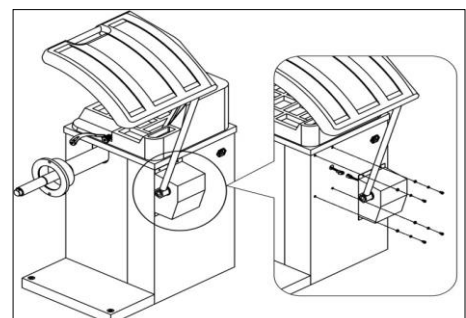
E01, E02 Conjunto de tornillo guía del eje
